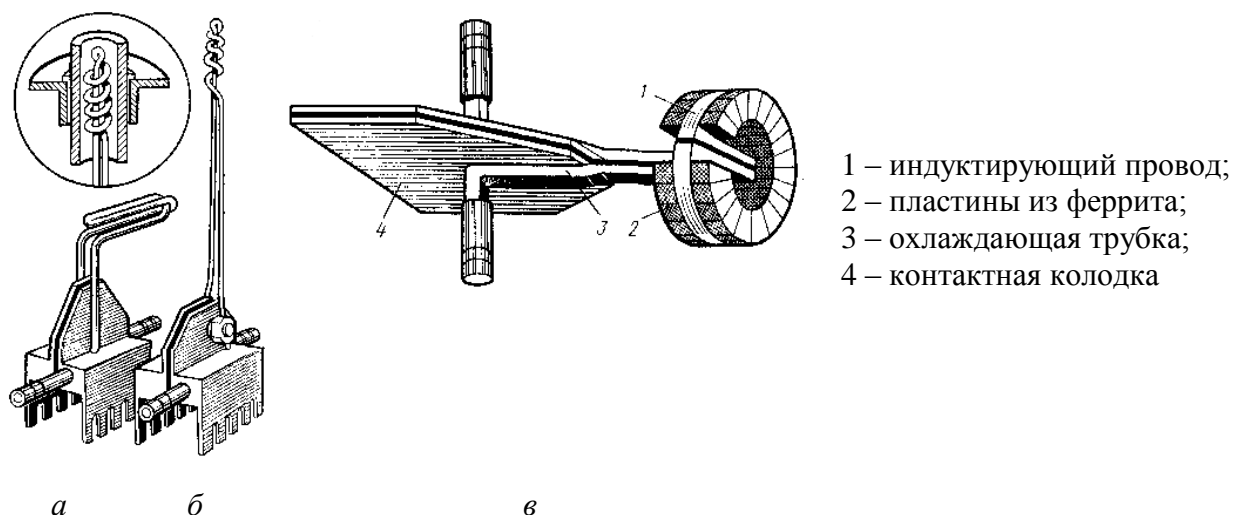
Индукторы для нагрева внутренних поверхностей:
